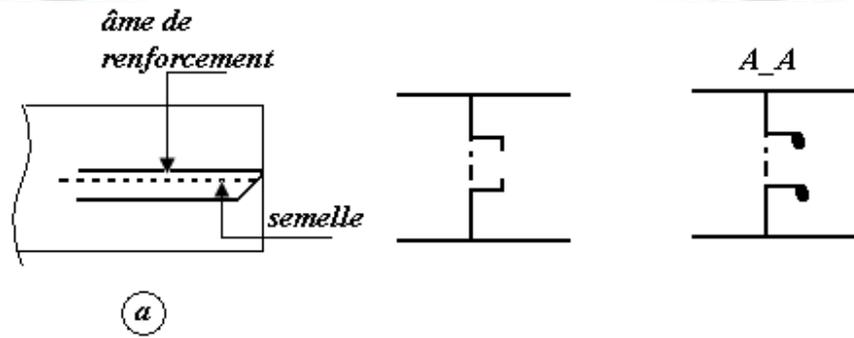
Renforcement de la carlingue centrale aux extrémités de navire.
